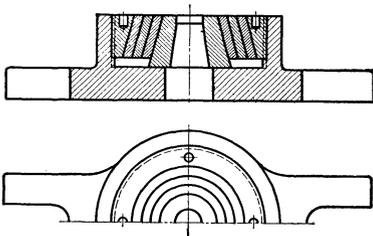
Auswechselbare Schnittplattenbefestigung.
